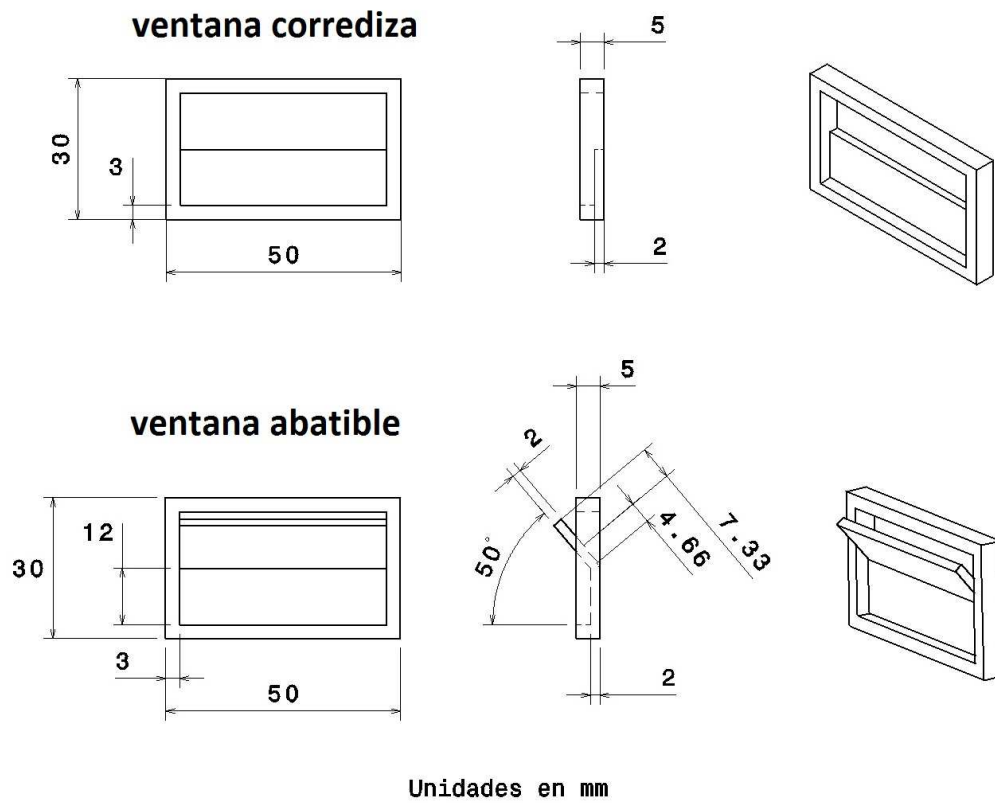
Planos de las ventanas construidas en acrílico. Elaboración propia.
